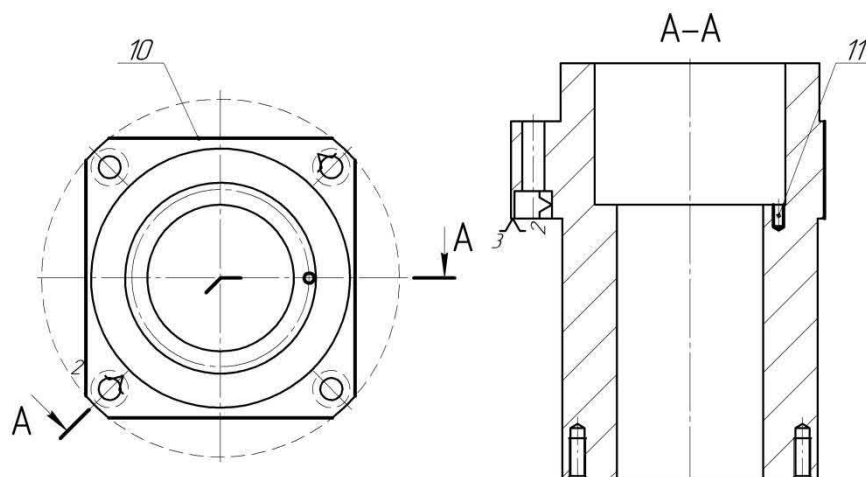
эскиз для фрезерной операции с ЧПУ 030 (установ. 2)
